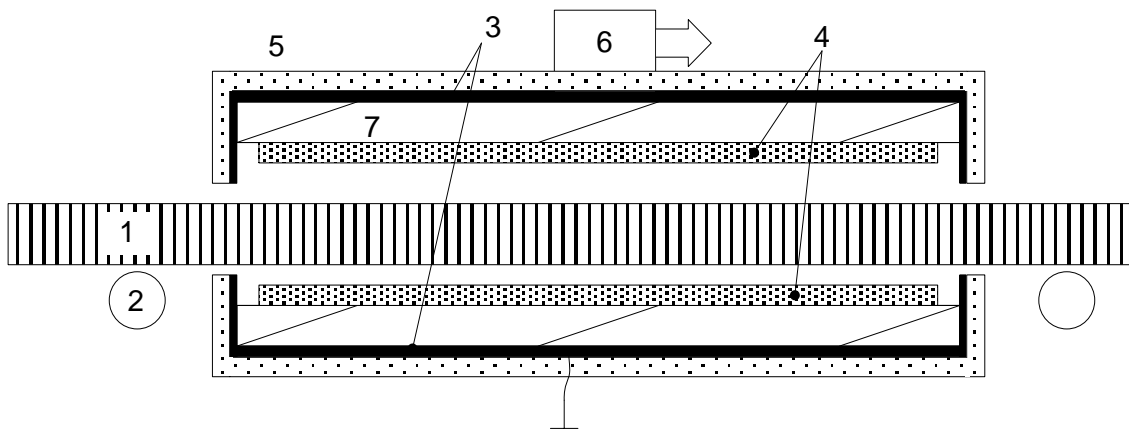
Конструкція перетворювача для визначення товщини полімерної плівки: 1 – плівка; 2 – ролик; 3 – корпус-екран; 4 – робочі пластини конденсатора; 5 – термостабілізаційна вставка; 6 – перетворювач; 7 – невідна основа.
